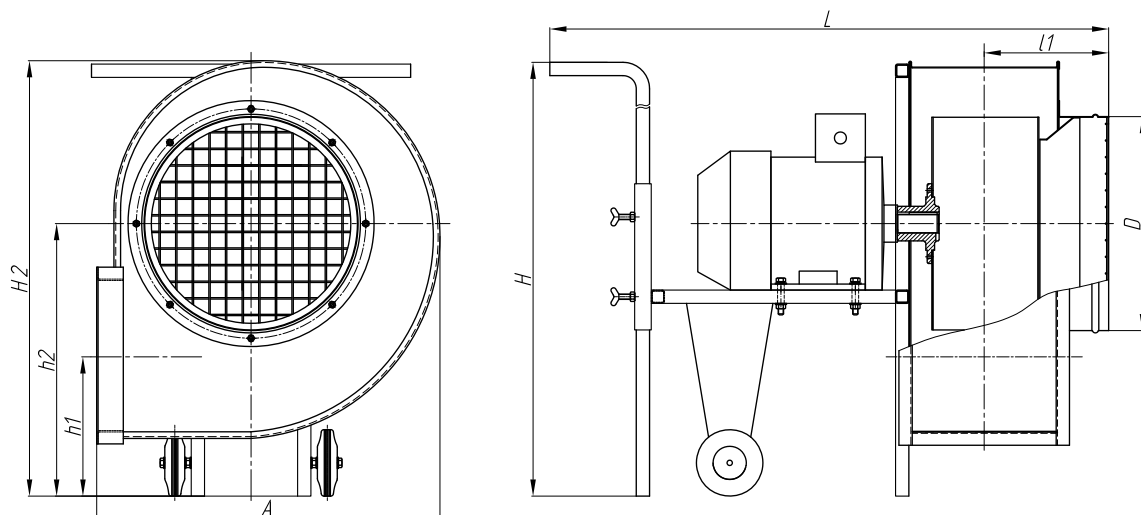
Габаритные и присоединительные размеры дымососов противопожарных электрических ДПЭ-ВЦ.
